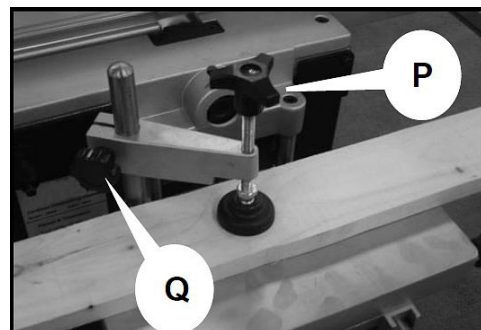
Werkstück mit Klemmvorrichtung fixieren
